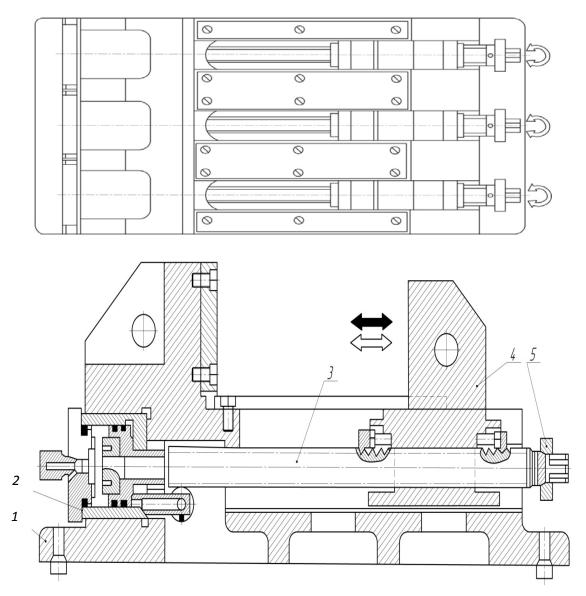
Трехпозиционное специализированное приспособление для установки заготовок гидропанелей: 1 – гидроцилиндр; 2 – корпус; 3 – винт; 4 – подвижная губка; 5 – рукоятка
